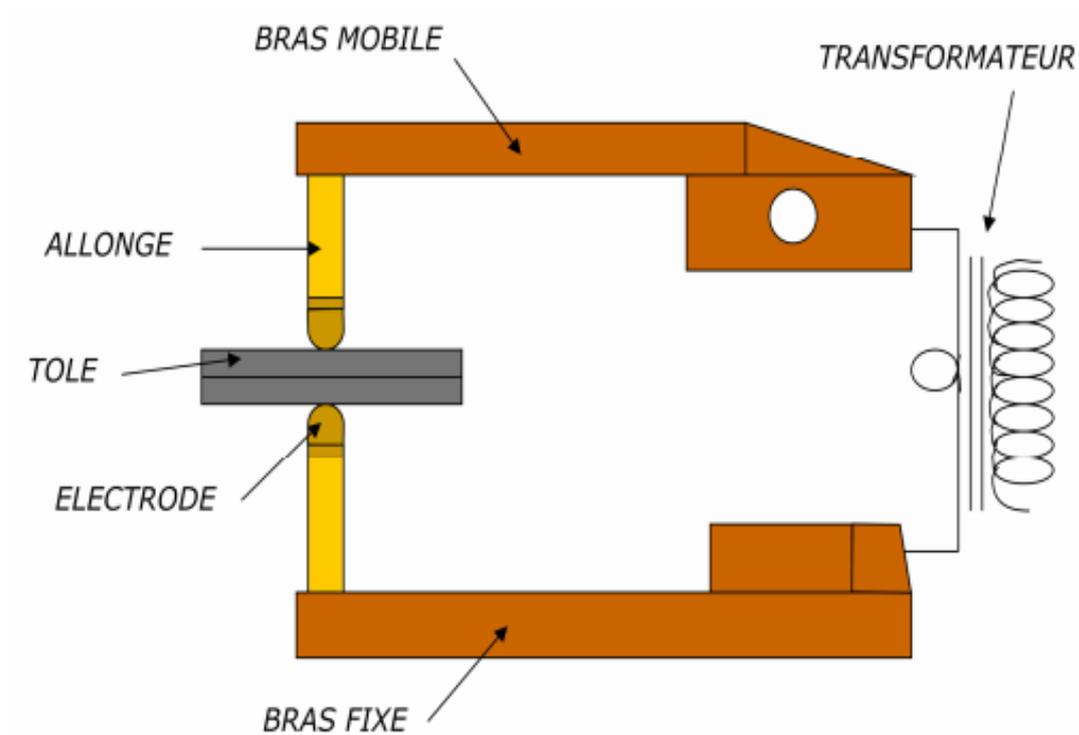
Mécanisme du soudage par point [7]
